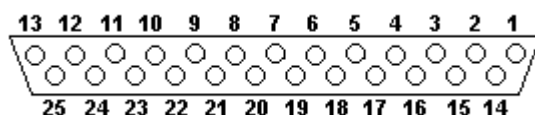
Conexão macho do conector DB-25 pelo lado da solda.
